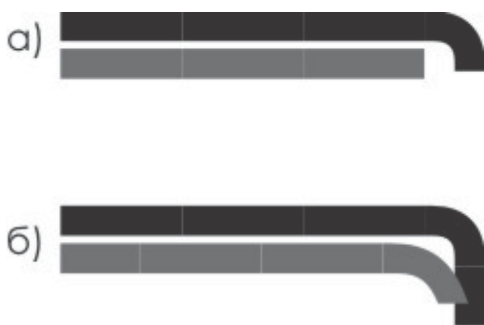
Принципиальная схема соединения деталей встык: а – простая стыковка, б – стыковка с натягом
